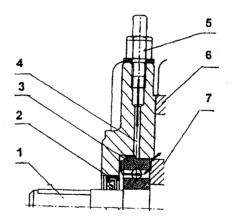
Схема подачи масла в корпус вакуумного насоса:
